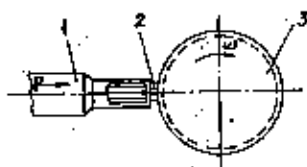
Схема упрочнения наплавленных образцов: 1-магнитоотрицательный преобразователь; 2-иглы-ударники; 3- цилиндрический образец с наплавкой
